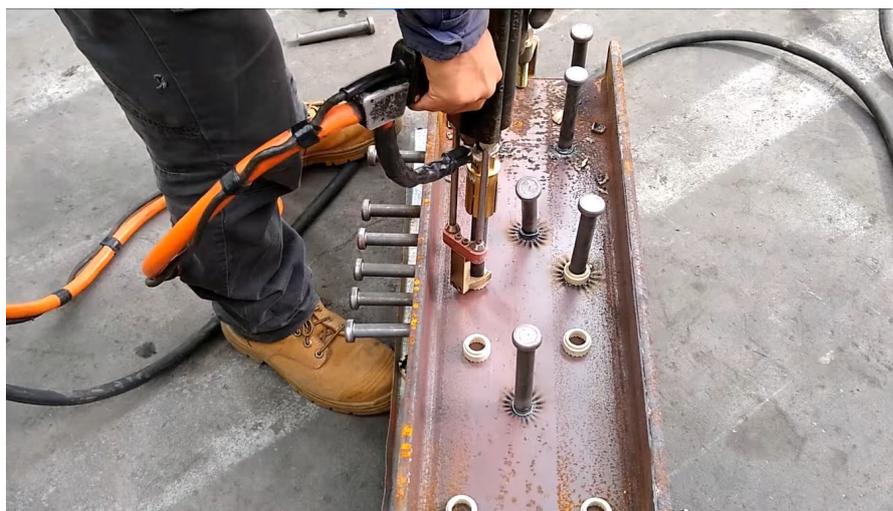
Soldadura especial con equipo Nelweld – 6000.
